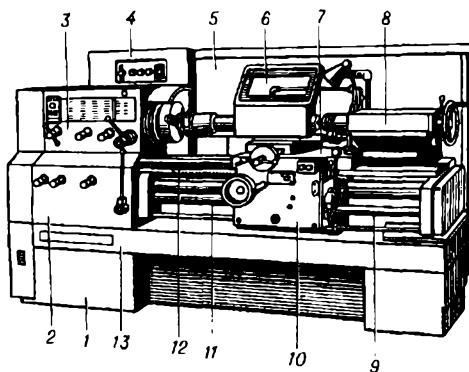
Токарно-винторезный станок: 1 – основание; 2 – коробка подач; 3 – передняя бабка; 4 – шкаф для электрооборудования; 5 – защитный экран; 6 – щиток; 7 – суппорт; 8 – задняя бабка; 9 – ходовой вал (для передачи движения при точении); 10 – фартук; 11 – ходовой винт (при нарезании резьбы); 12 – станина; 13 – крыто
